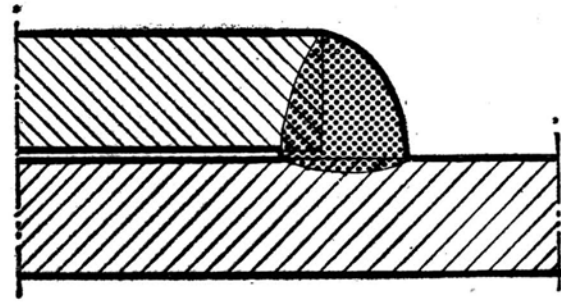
SOLDADURA DE ANGULO EN SOLAPE
